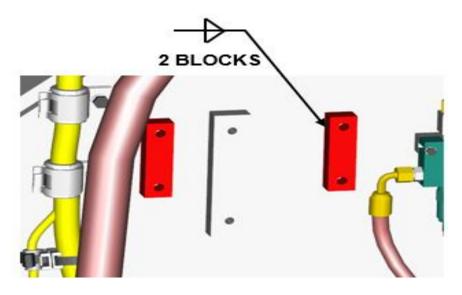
Ubicación de bloques para soporte de base de filtros y proceso de soldadura
